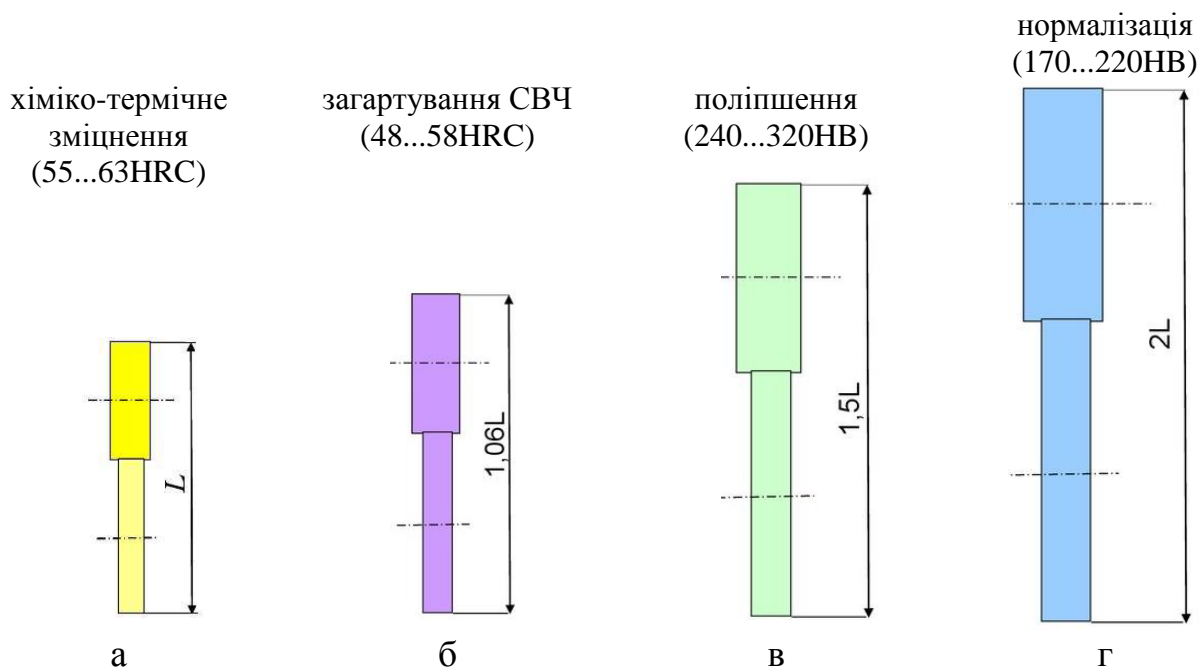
Габарити передачі залежно від виду термообробки і твердості робочої поверхні зубців
